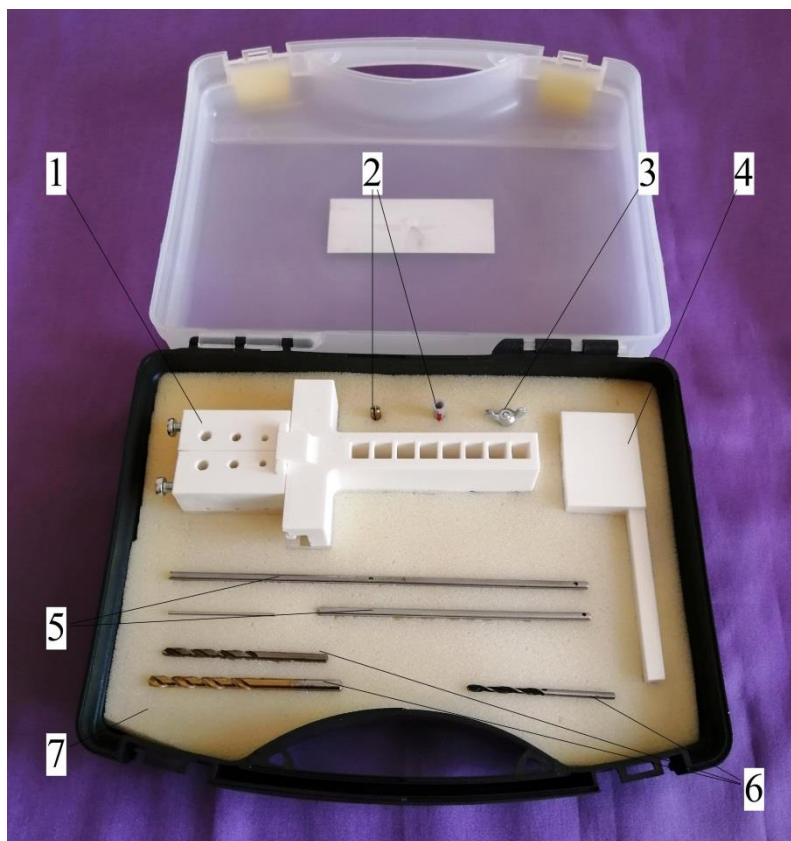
Внешний вид устройства в кейсе для переноски: 1 – блок для позиционирования сверл, 2 – фиксаторы, 3 – стопорный винт, 4 – боковой блок, 5 – направляющие, 6 – сверла, 7 – кейс
